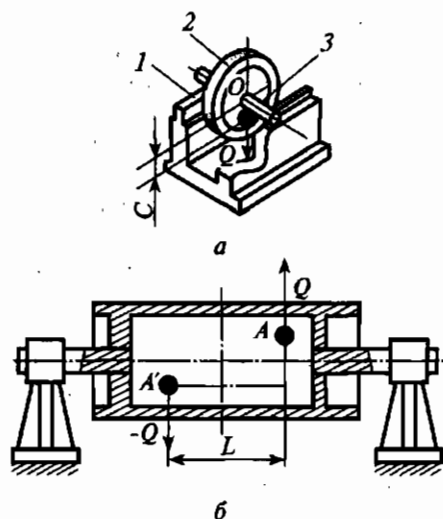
Схемы статической (а) и динамической (б) балансировки деталей: 1 — опорная поверхность; 2 — диск; 3 — оправка
